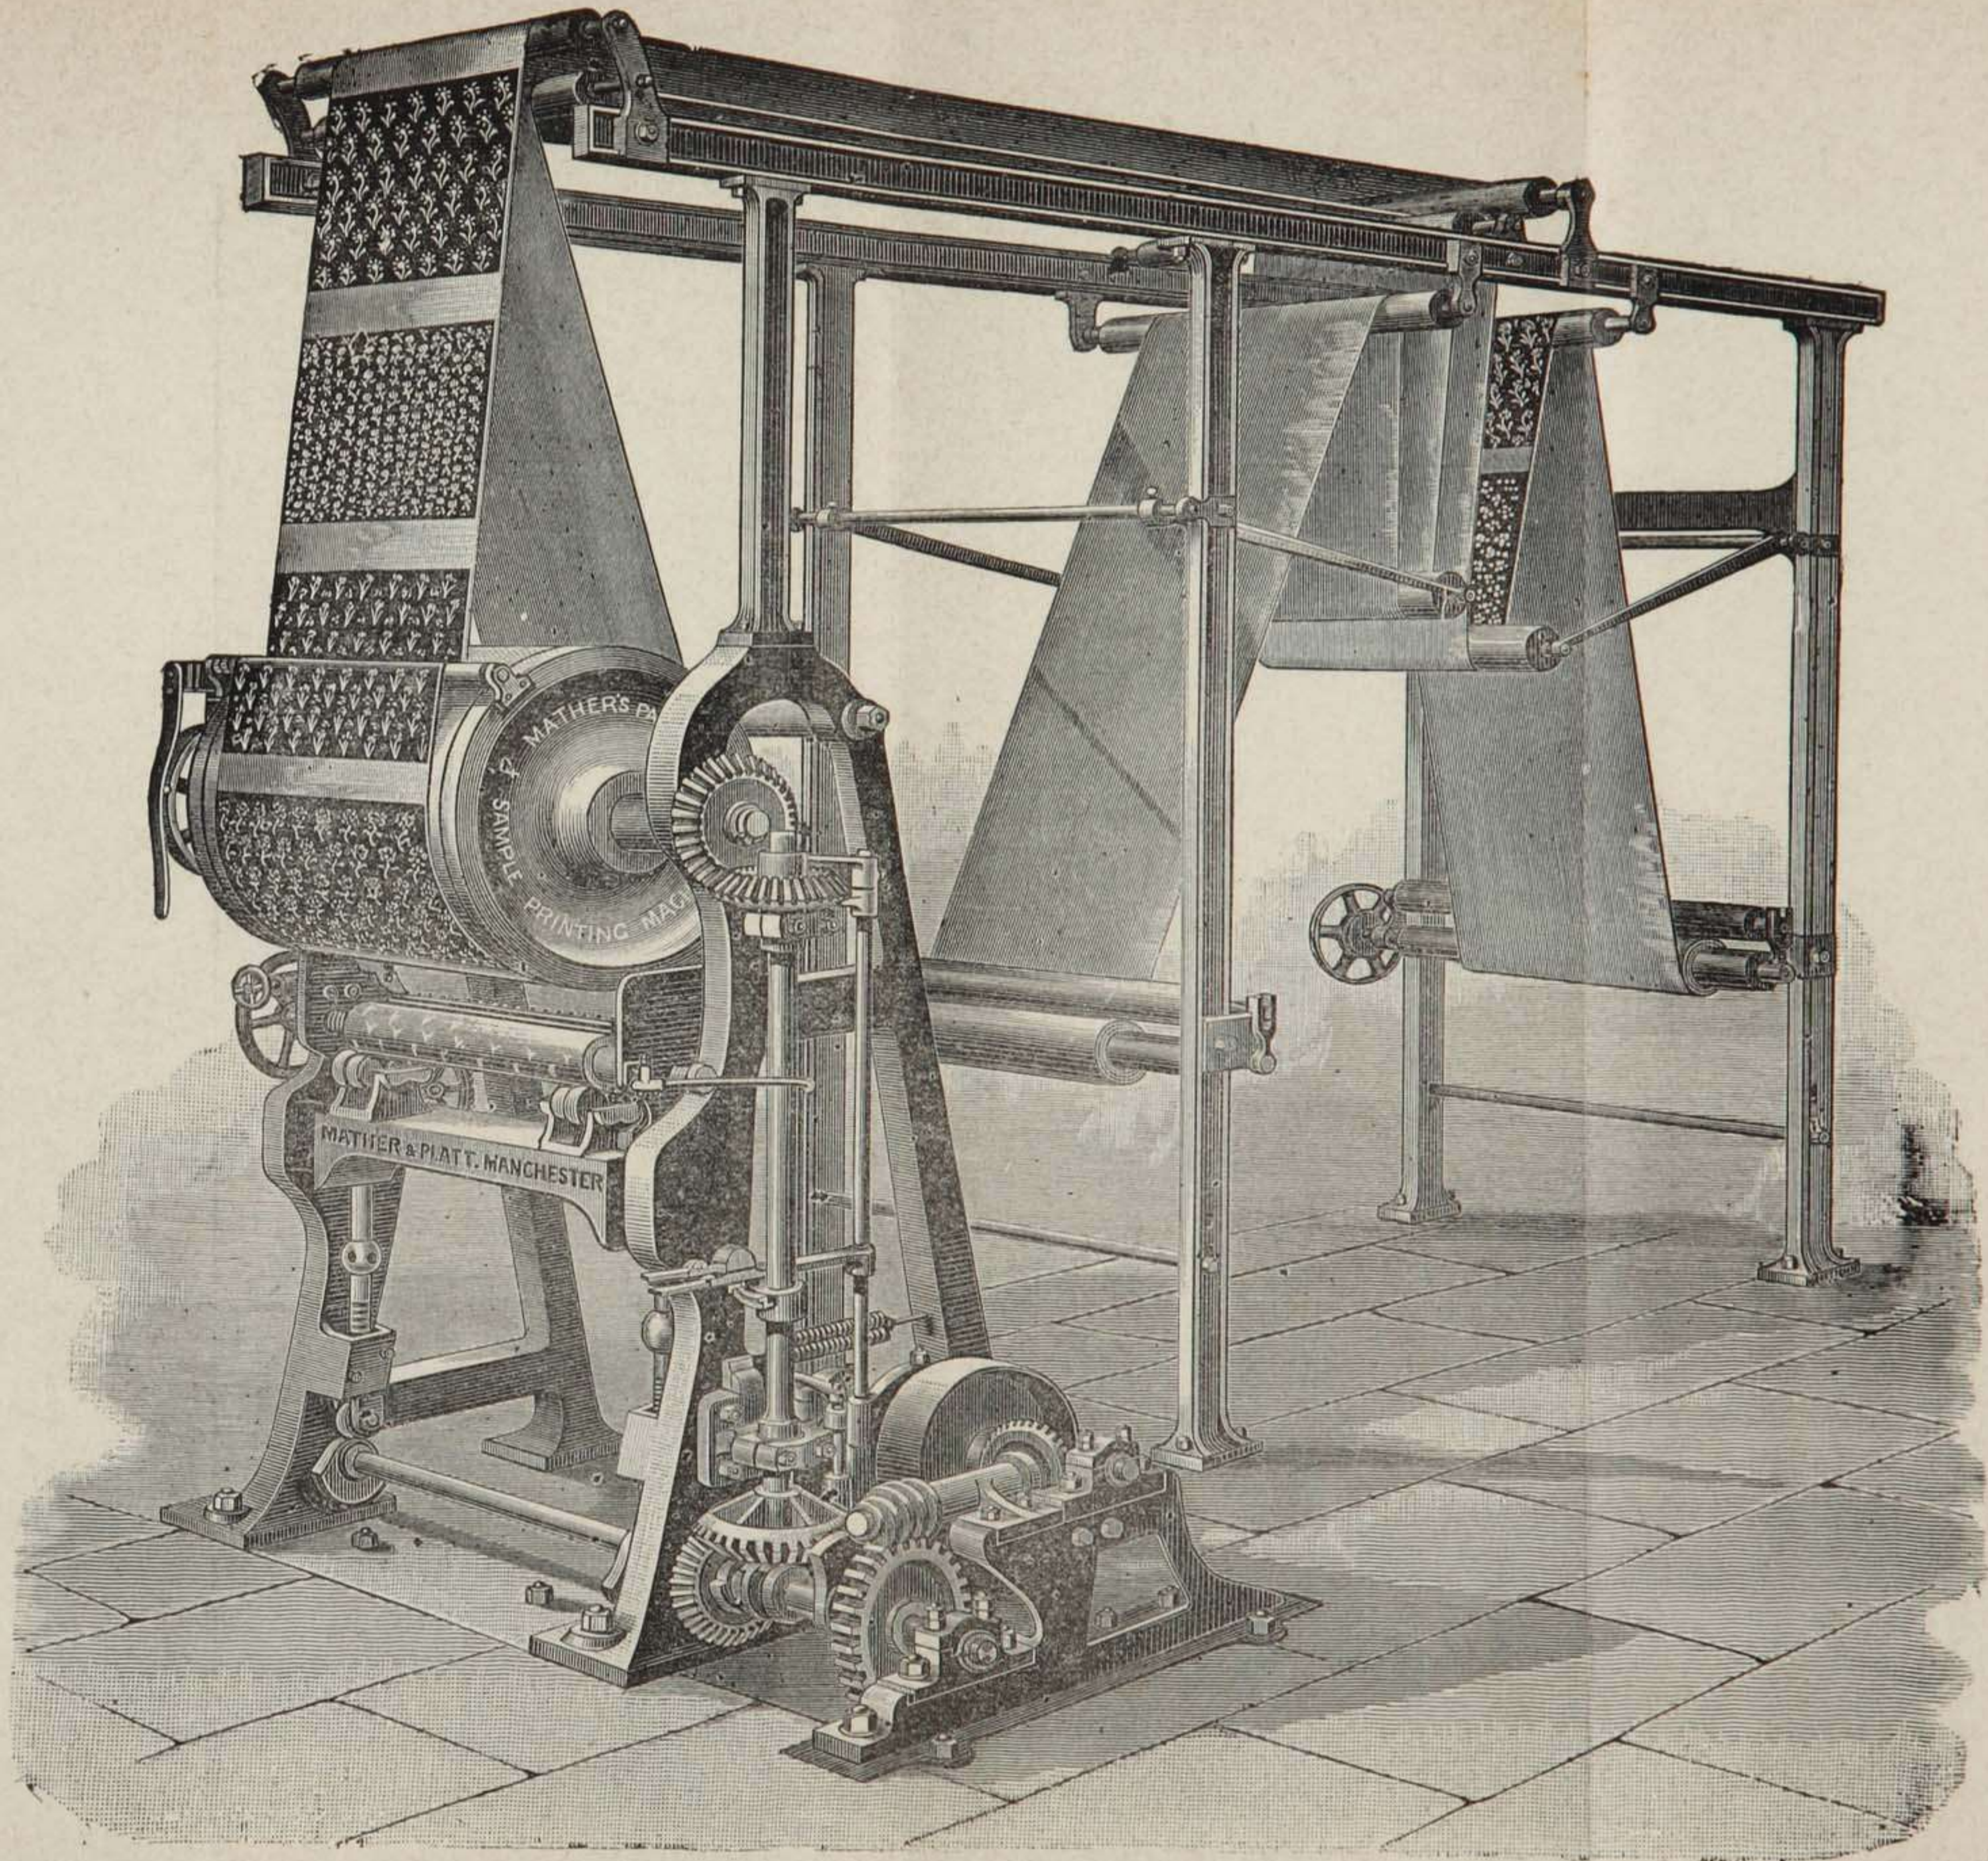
Machine à imprimer les échantillons de MATHER & PLATT
